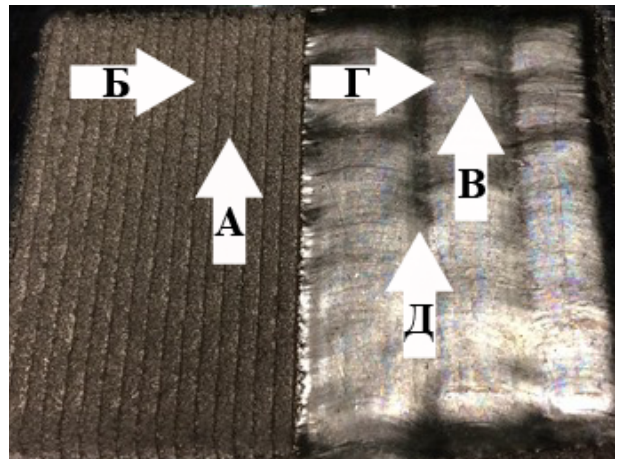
Схема измерения шероховатости поверхности полученных образцов
